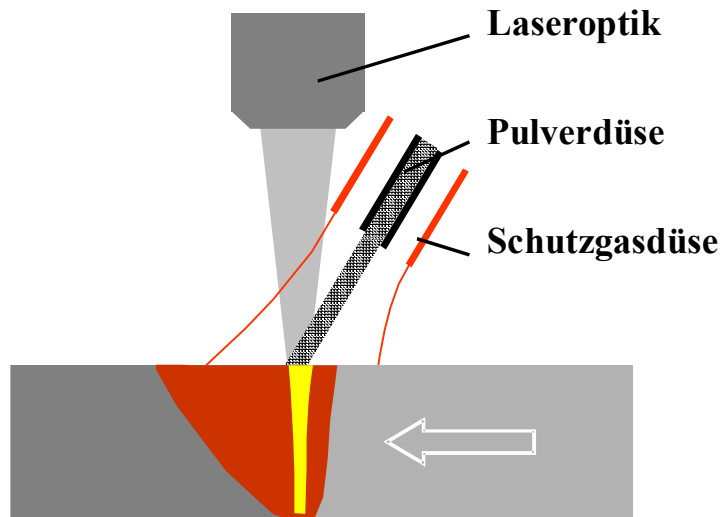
Laserschweißen mit der Pulvertechnologie
